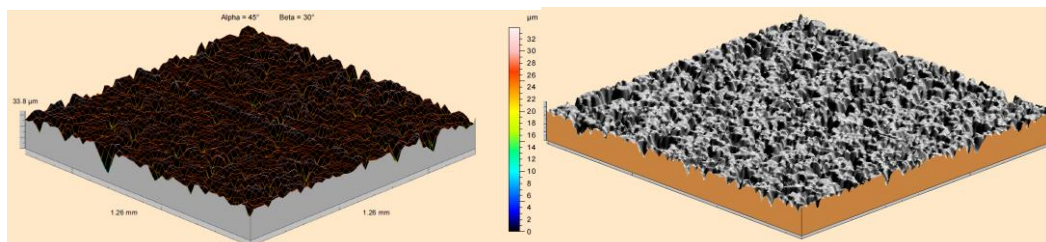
Вид трехмерного изображения поверхности детали из низколегированного материала
